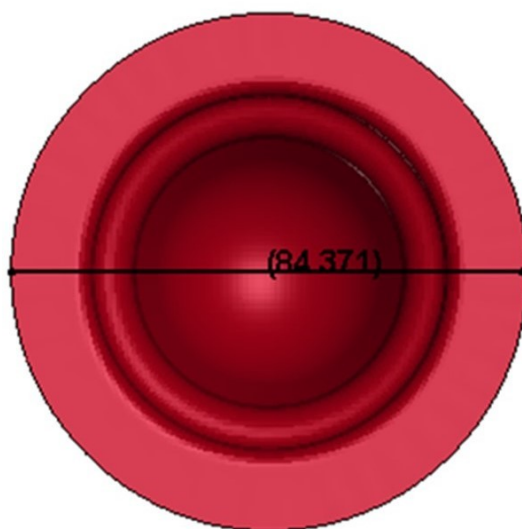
Диаметр фланца из заготовки 100 мм
